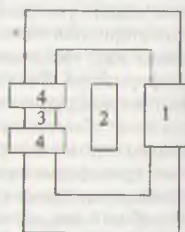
Сварочные трансформаторы СТАН и СТШ: 1-реактивная катушка; 2-магнитный шунт; 4-первичная обмотка.
